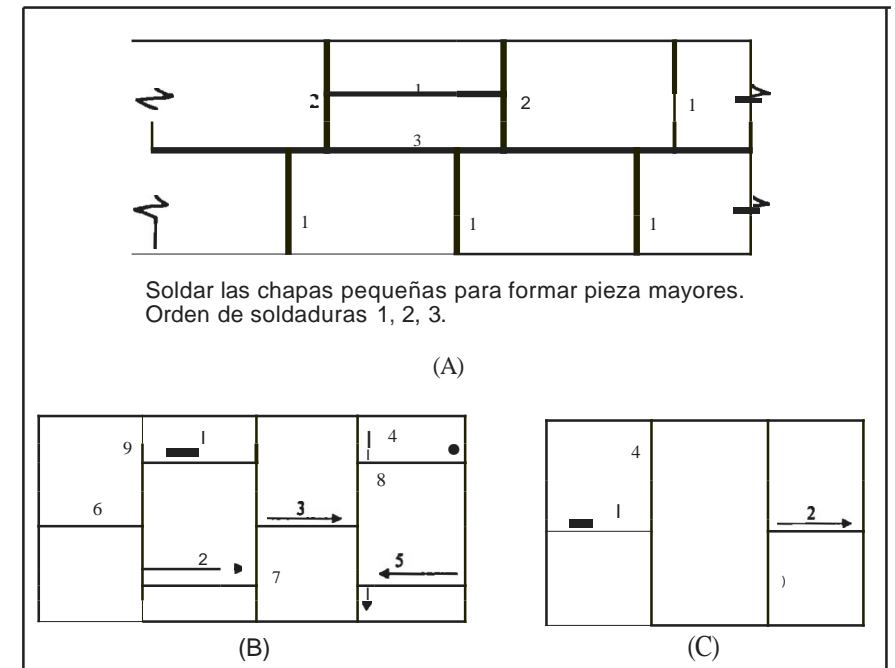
SOLDEO DE UN CONJUNTO DE CHAPAS
